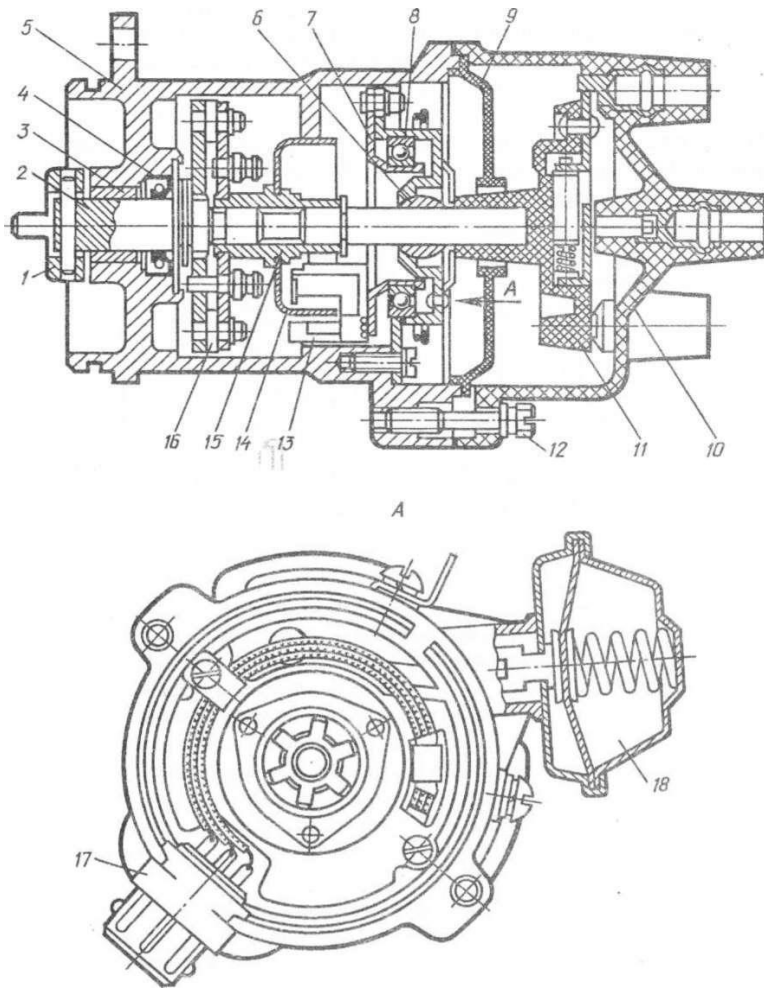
Датчик-розподільник 40.3 706: 1 - муфта; 2 - вал; 3,6- втулки; 4 - сальник; 5 - корпус; 7 - рухома пластина; 8 - підшипник; 9 - перегородка; 10 - кришка; 11 - бігунець; 12 - гвинт; 13 - датчик Холла; 14 - ротор-шторка; 15 - втулка; 16- відцентровий регулятор; 17 - штекер; 18- вакуумний регулятор
